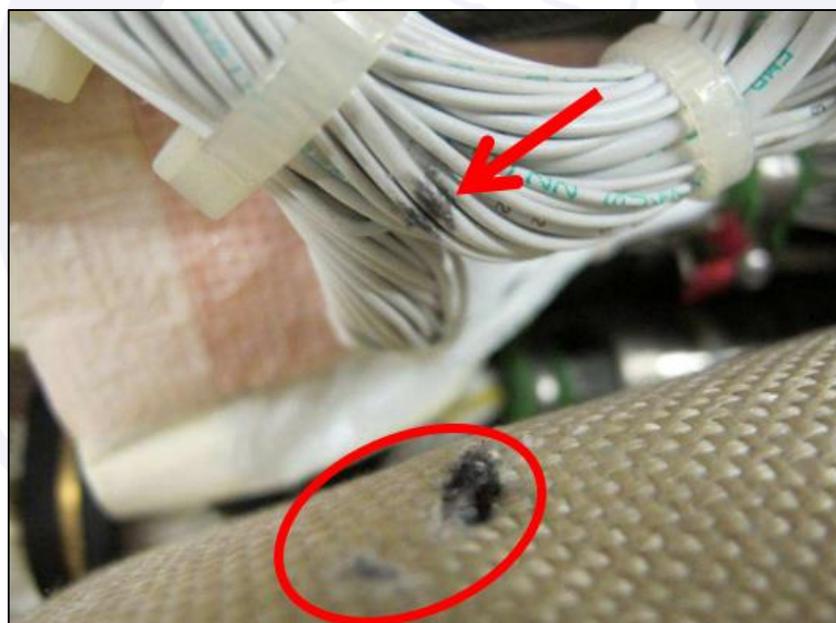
Sinal de atrito entre a cablagem e a calha do lado direito do PR-AUM.
